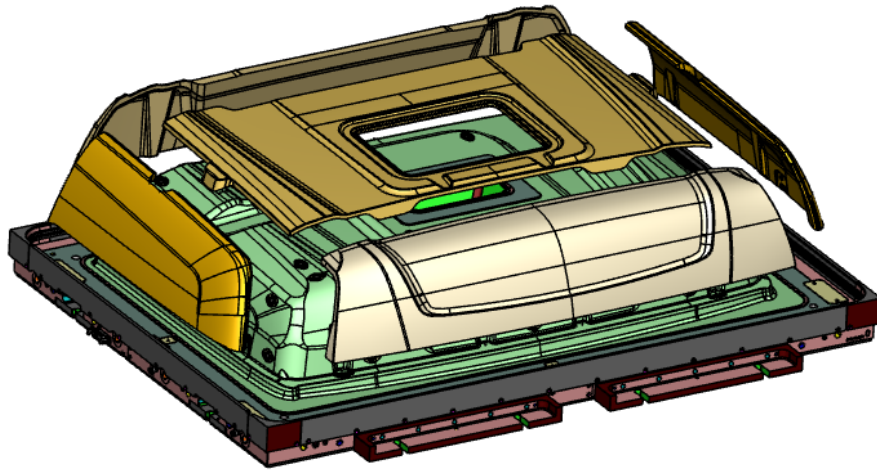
Oberwerkzeug (Stempel) inkl. Schaumkerne (gelb), welche über Magnete gehalten werden
